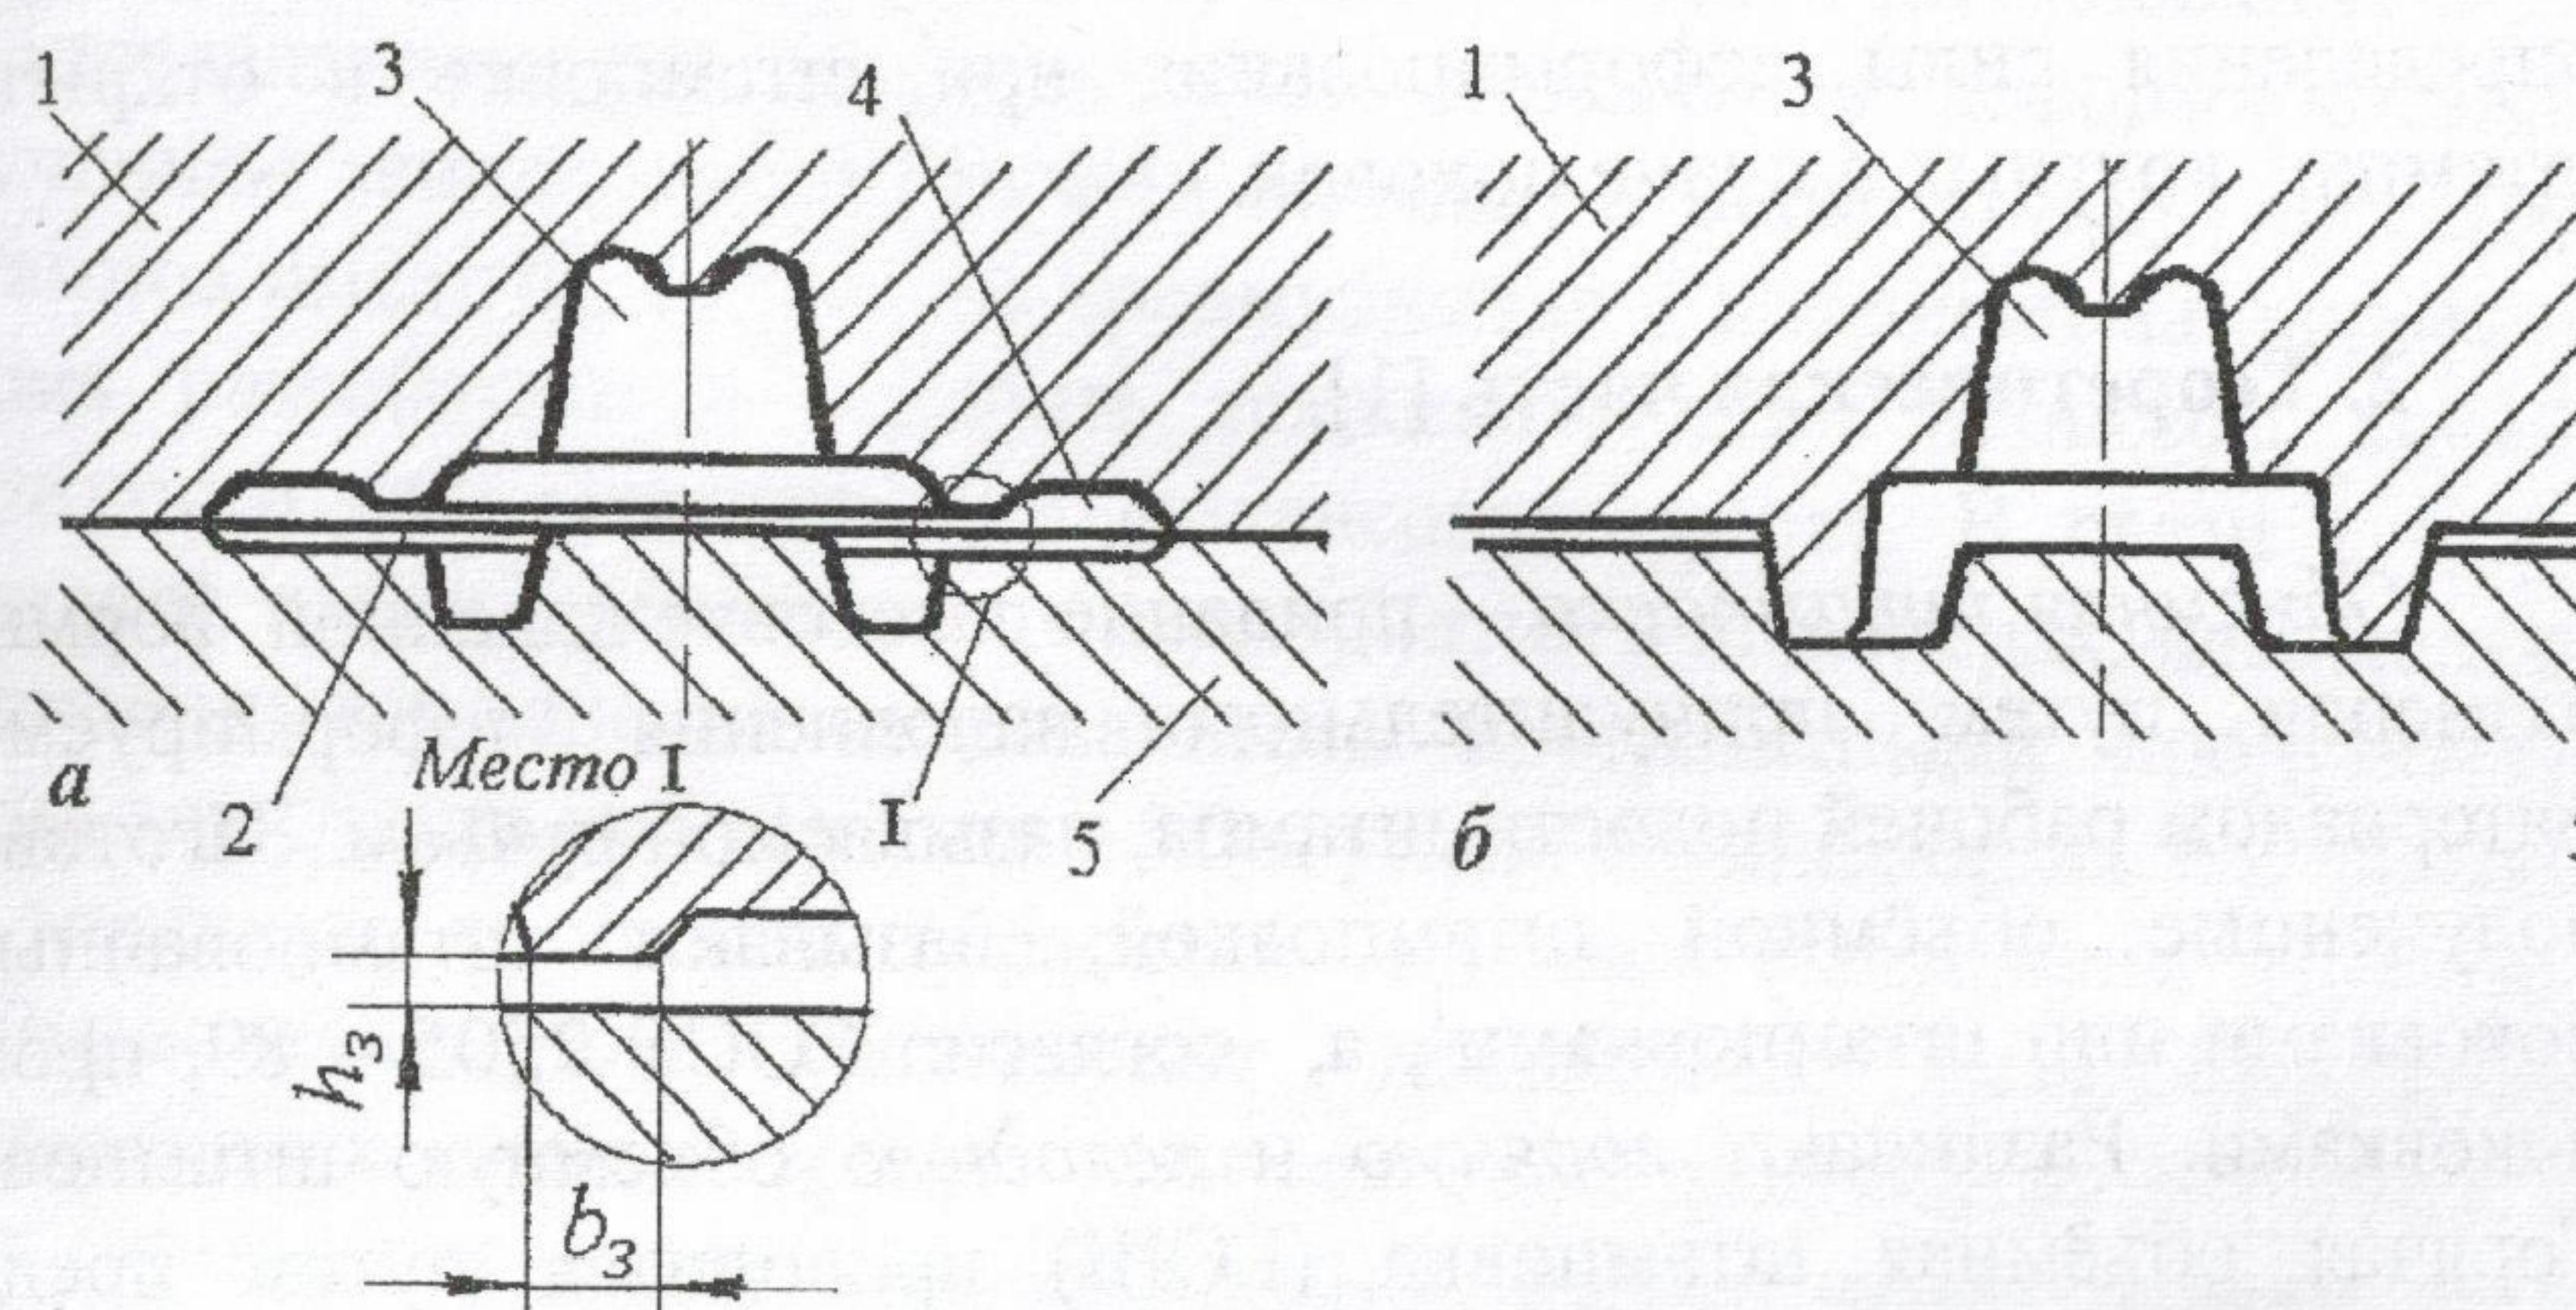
Схемы горячей объемной штамповки: а – открытый штамп для штамповки с облосом; б – закрытый штамп для безоблойной штамповки; 1 – верхняя часть штампа; 2 – мостик облойной канавки; 3 – ручей штампа; 4 – магазин; 5 – нижняя часть штампа
